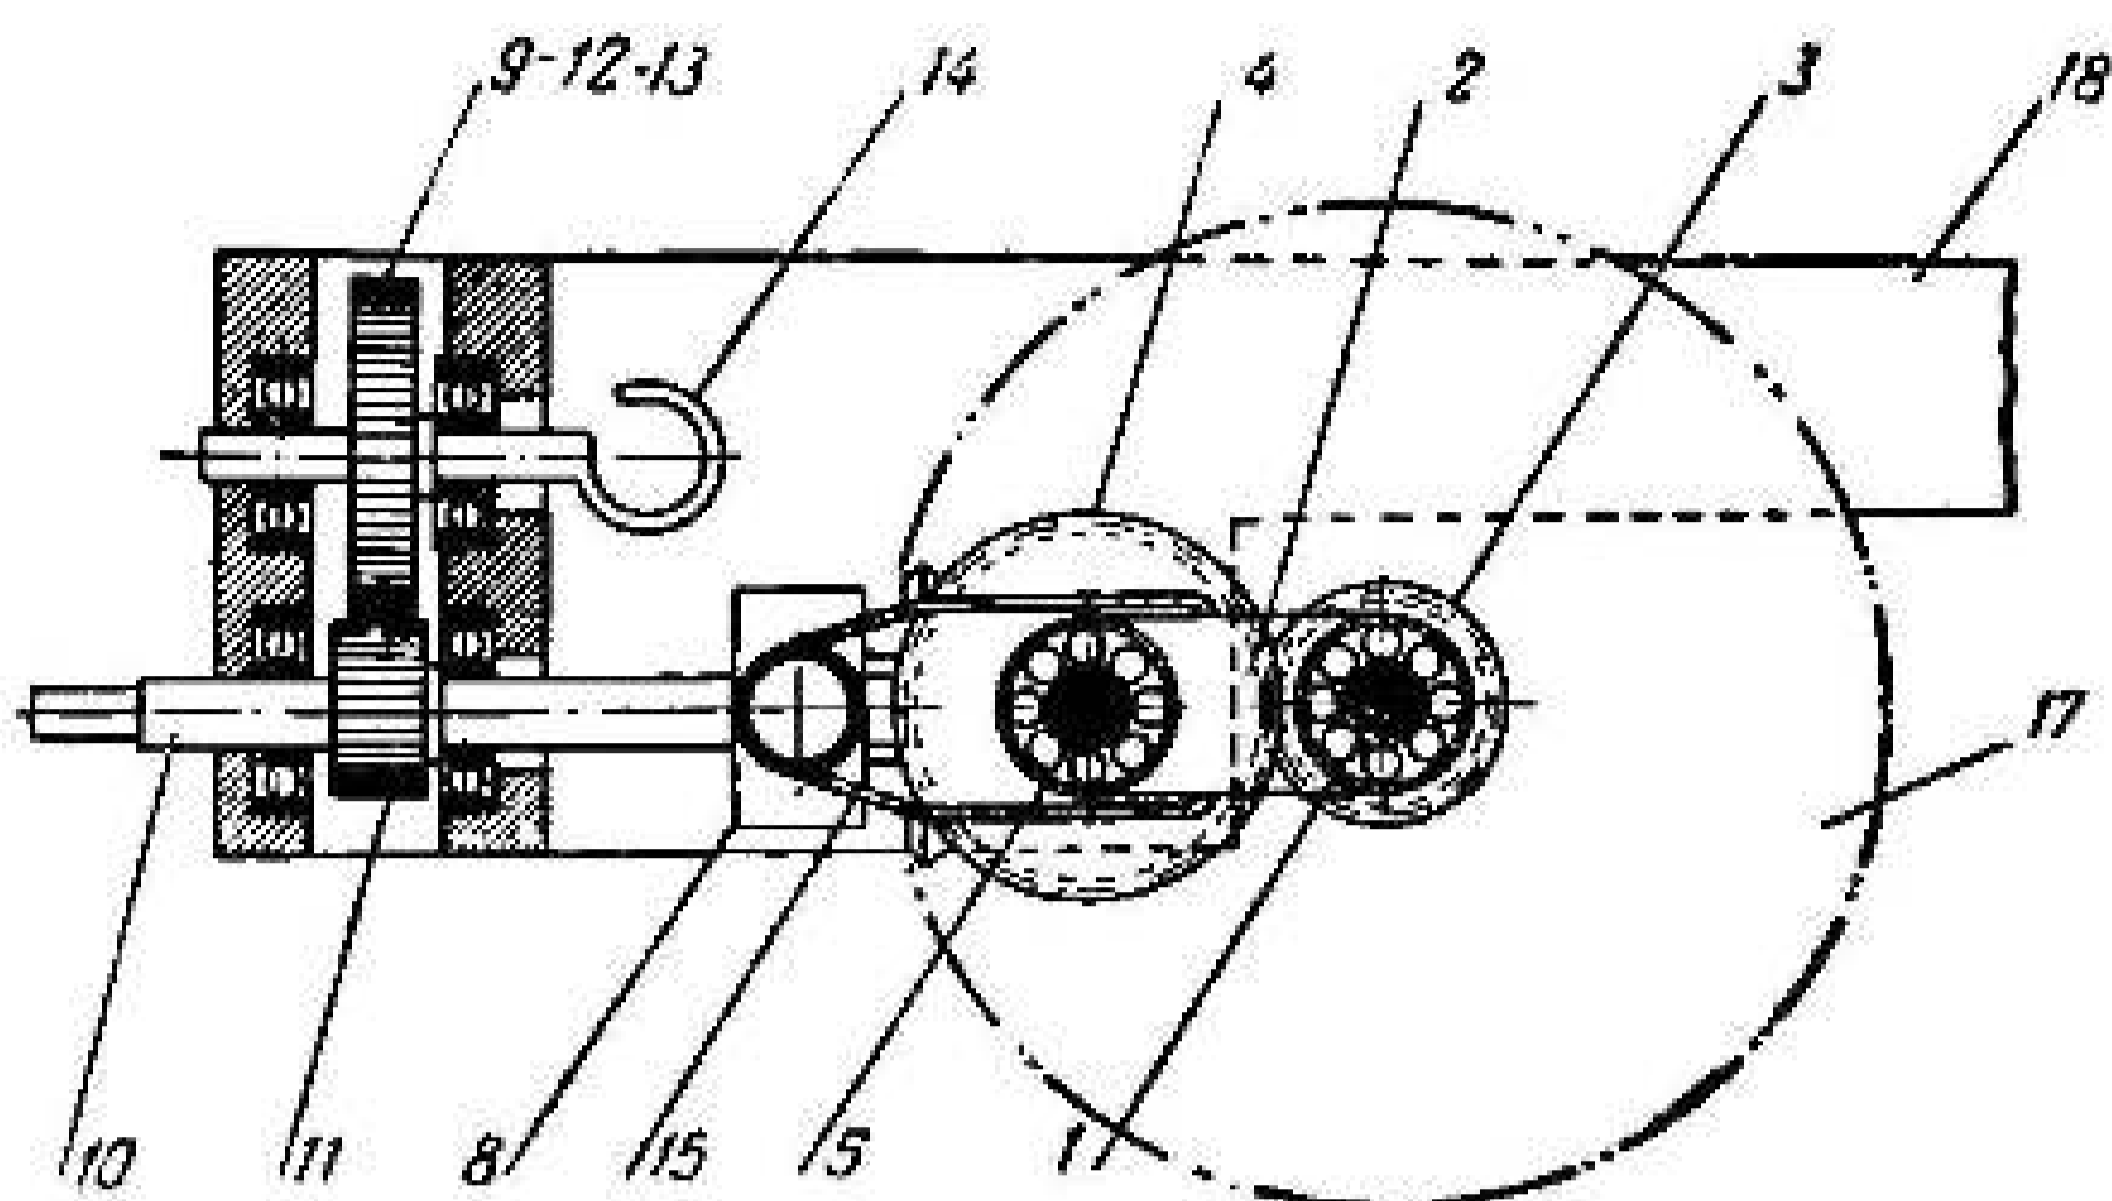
Схема силовой передачи и подвески ведущих колес: 1 — ведущая ось; 2 — рычаг-балансир; 3 — малая цилиндрическая шестерня; 4 — большая цилиндрическая шестерня; 5 — промежуточный поперечный вал; 8 — опора промежуточного поперечного вала; 9, 12 и 13 — цилиндрические шестерни параллельно работающих резиновых двигателей; 10 — промежуточный продольный вал; 11 — малая цилиндрическая шестерня; 14 — ось с крюком; 15 — пружина; 17 — ведущее колесо; 18 — рама модели
